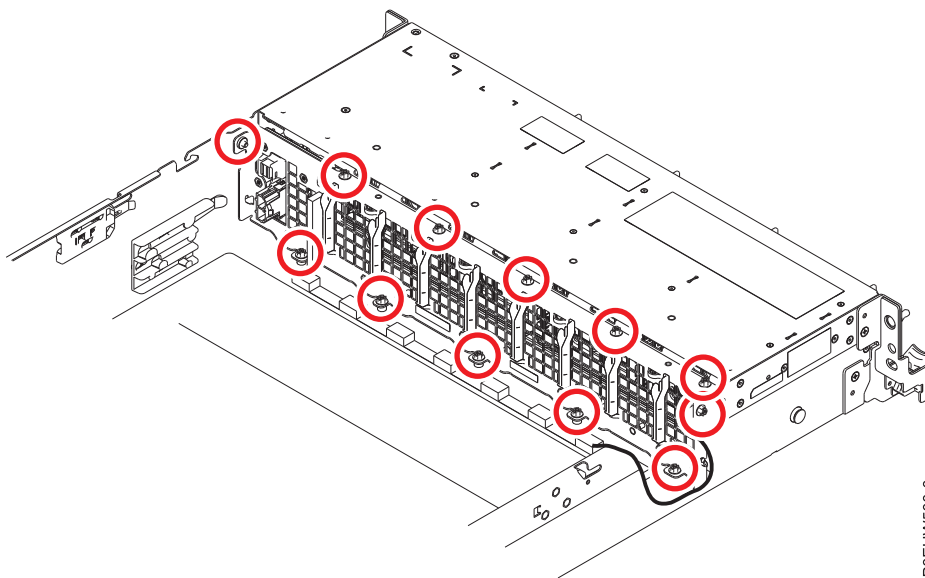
Emplacement des vis de la carte des ventilateurs et des unités de disque
